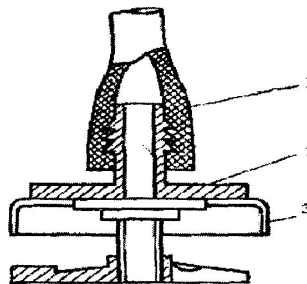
Пристрій для під'єднання шланга від калібратора до горловини радіатора: 1 - шланг від калібратора К-69М; 2 - пробка;
